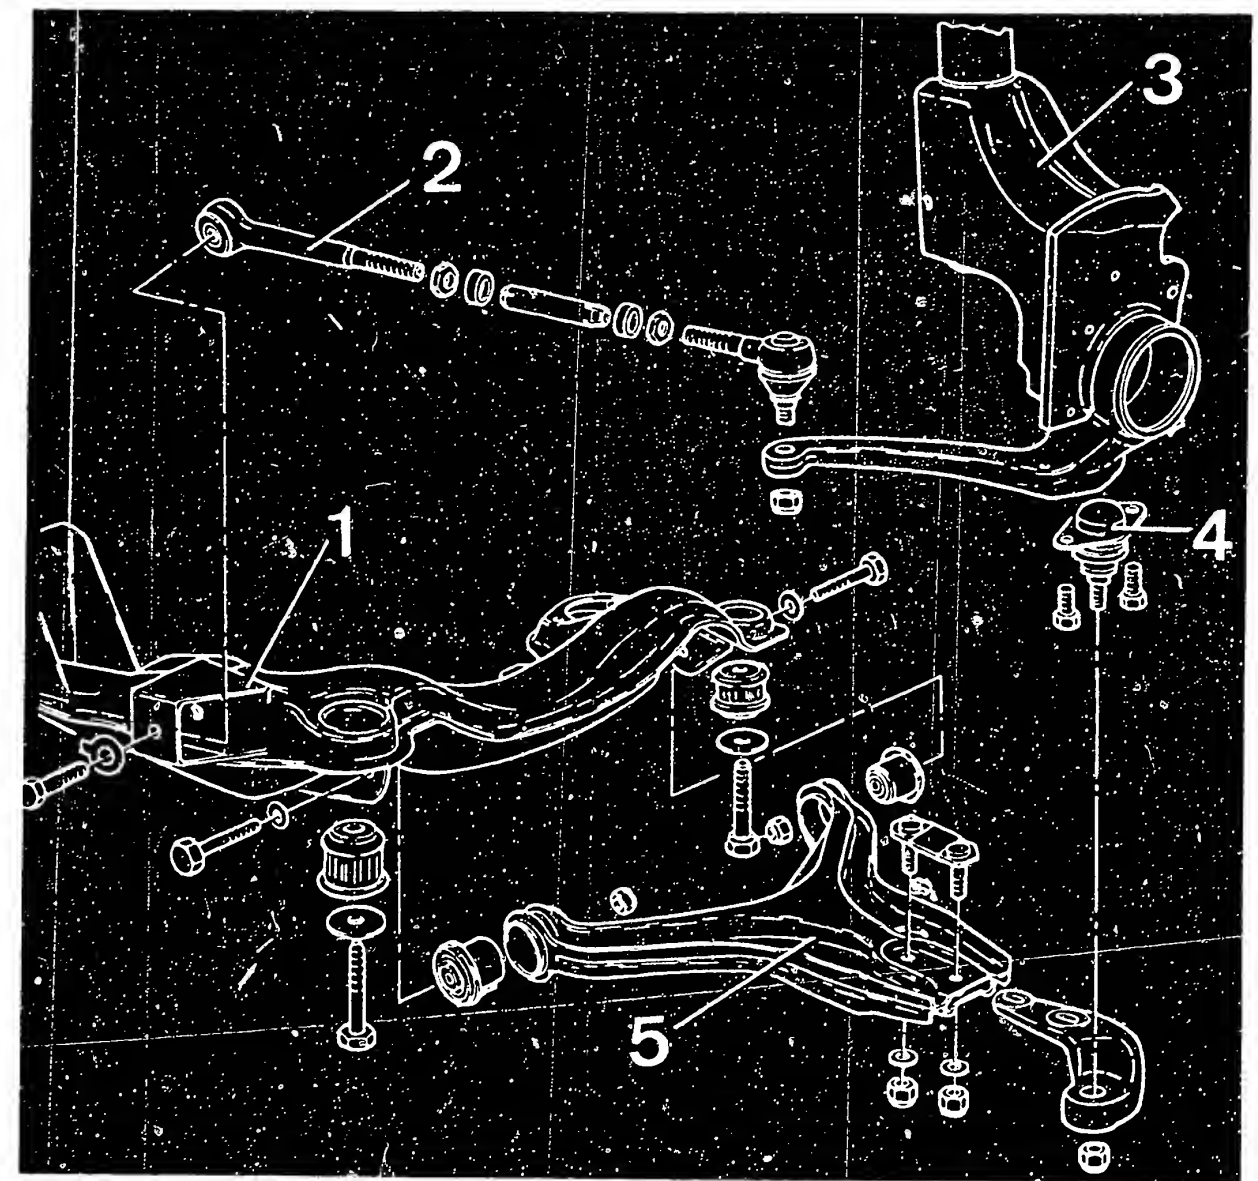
Einzelteile der Hinterradaufhängung 1 Aggregatenträger – 2 Spurstange – 3 Radlagergehäuse – 4 Kugelgelenk – 5 Querlenker.
